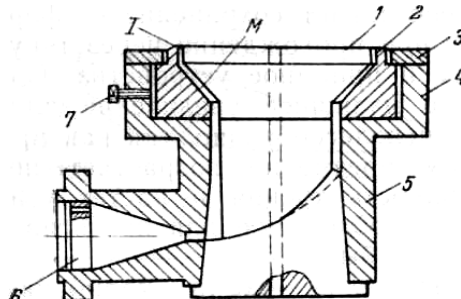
Схема кутової головки з боковим введенням розплаву: 1 – дорн; 2 – матриця; 3 – кільце; 4 – корпус; 5 – дорнотримач; 6 – решітка; 7 – регулювальні гвинти; I – формуючий зазор; M – дифузійний канал
